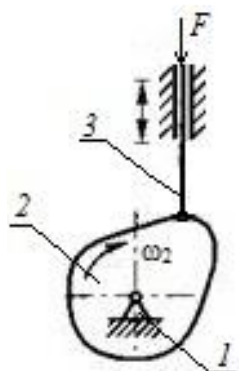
Кулачковий механізм: 1 – стояк; 2 – кулачок; 3 – штовхач.
